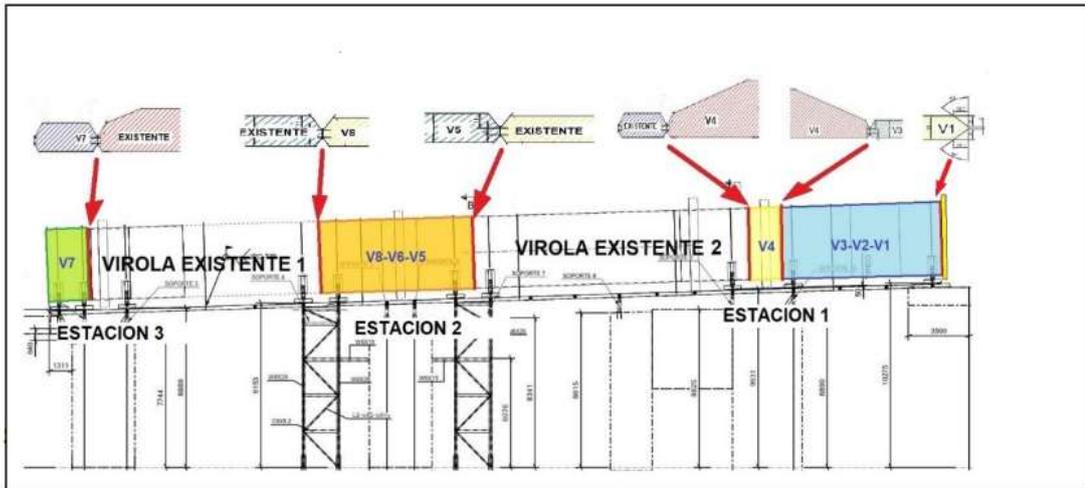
Diagrama polar y puntos de gramilado en el horno, juntas de soldadura
